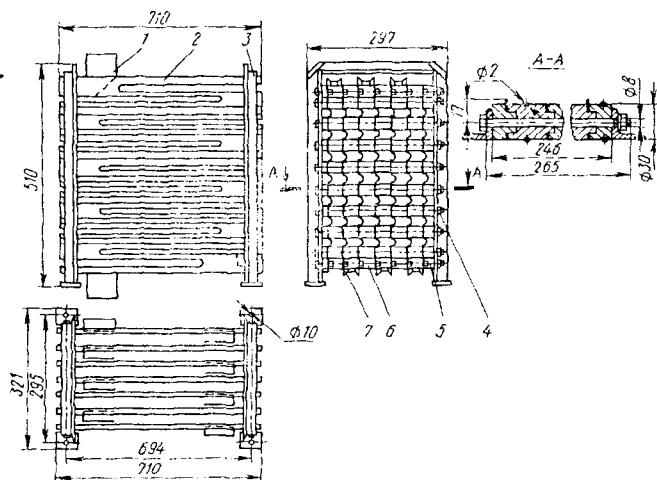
Пластинчатый (пакетный) нагреватель: 1 – выводная клемма; 2 – нагревательный лист; 3 – рамка каркаса; 4 – стяжной болт; 5 – крайний изолятор; 6 – средний изолятор; 7 – промежуточная клемма.
